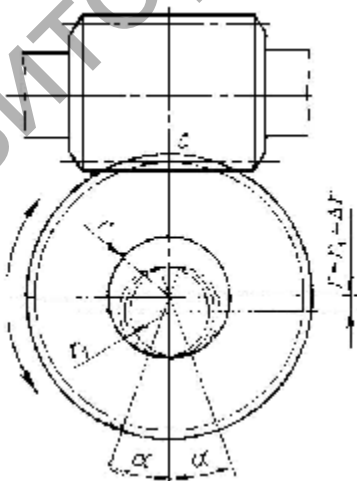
Радиальный зазор в подшипниках червячного колеса [39]
